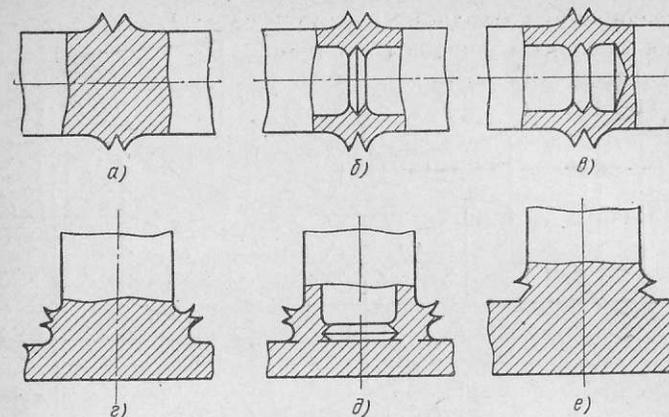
Типы сварных соединений сварки трением:
